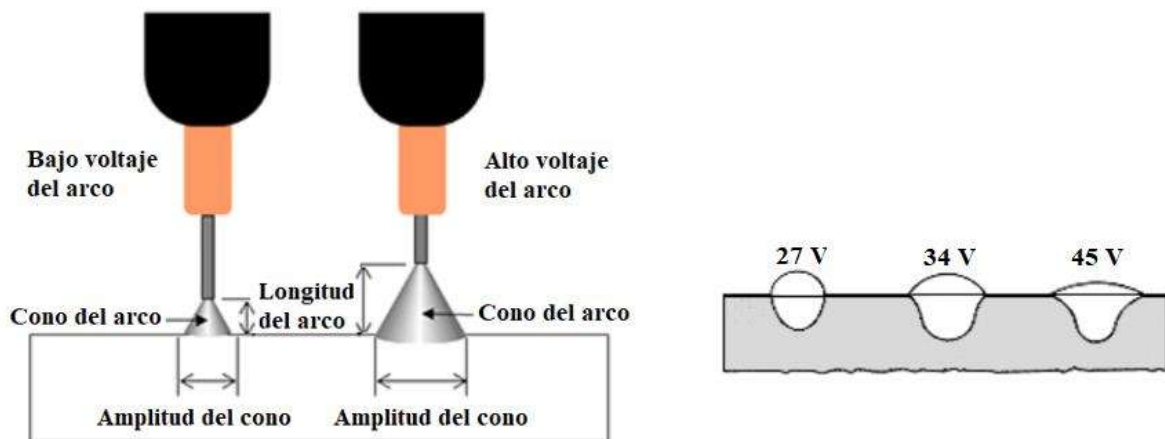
Efecto del voltaje del arco sobre la forma y penetración del cordón de soldadura.
